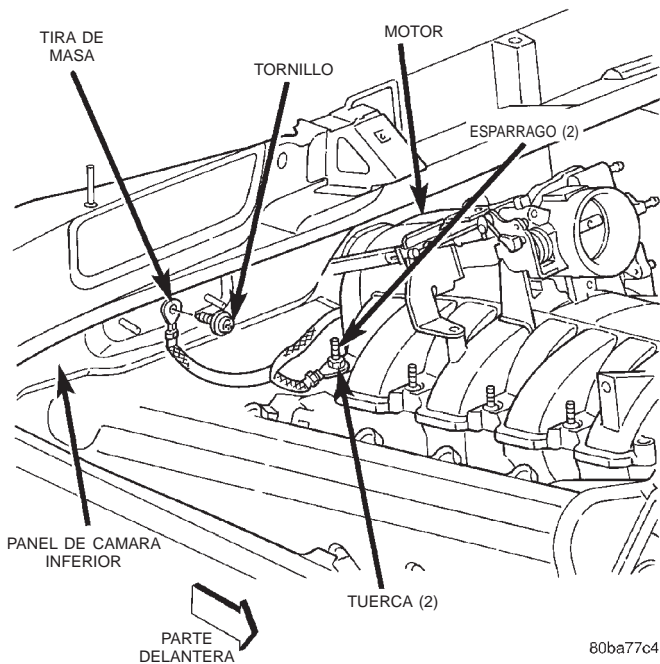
Desmontaje e instalación de la tira de masa del motor a la carrocería - Motor 4.7L
